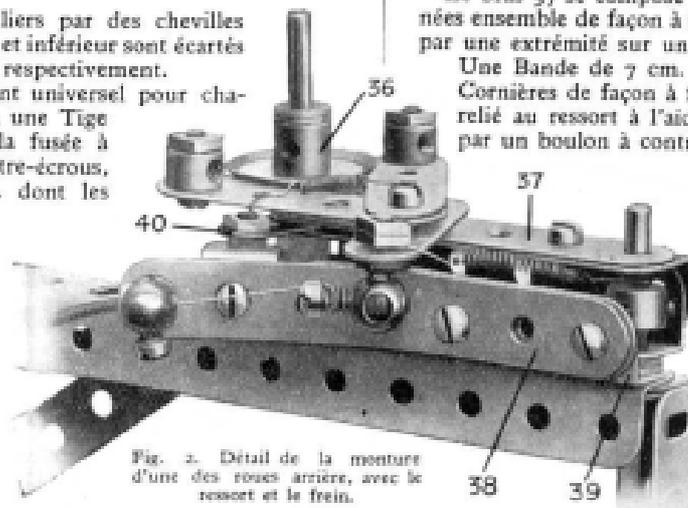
Détail de la monture d'une des roues arrière, avec le ressort et le frein.
